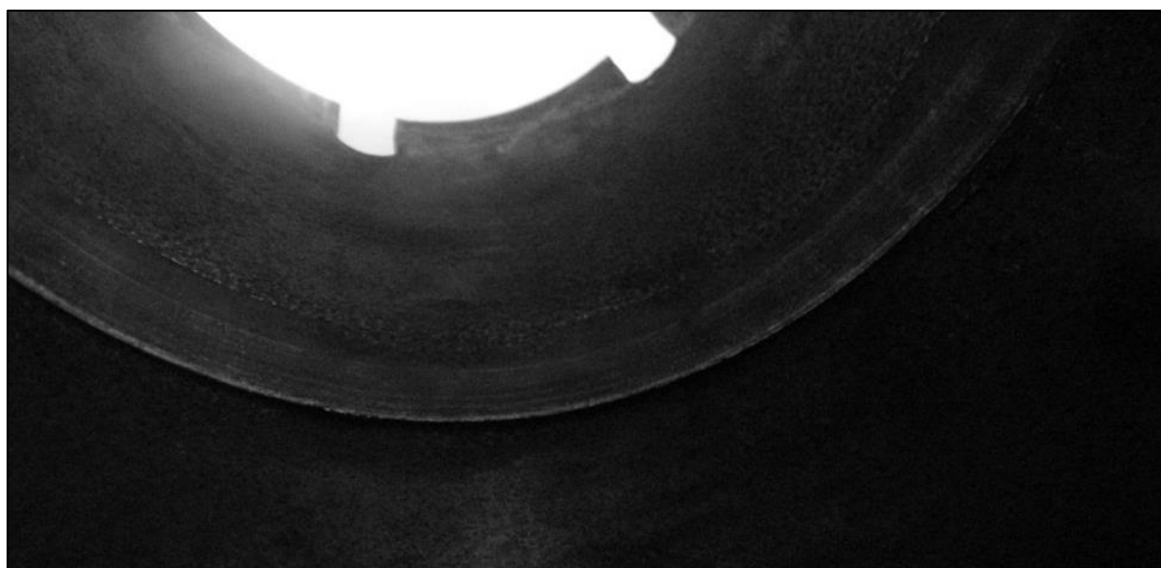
Desnível interno entre o anel utilizado para a solda e os tubos detectado por inspeção visual.
